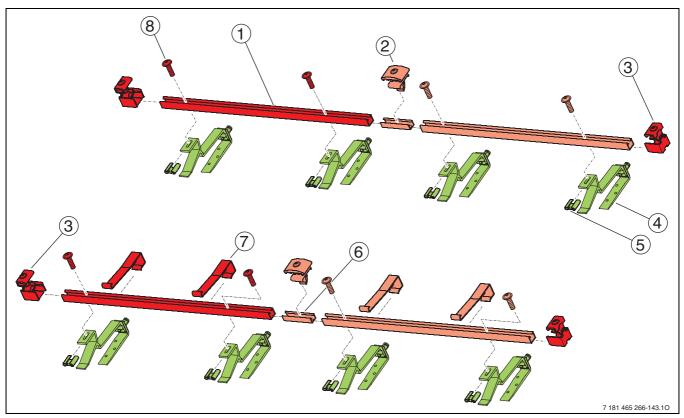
Grundmontage-Set und Erweiterungs-Set Aufdach mit Dachanbindung (2 x)
